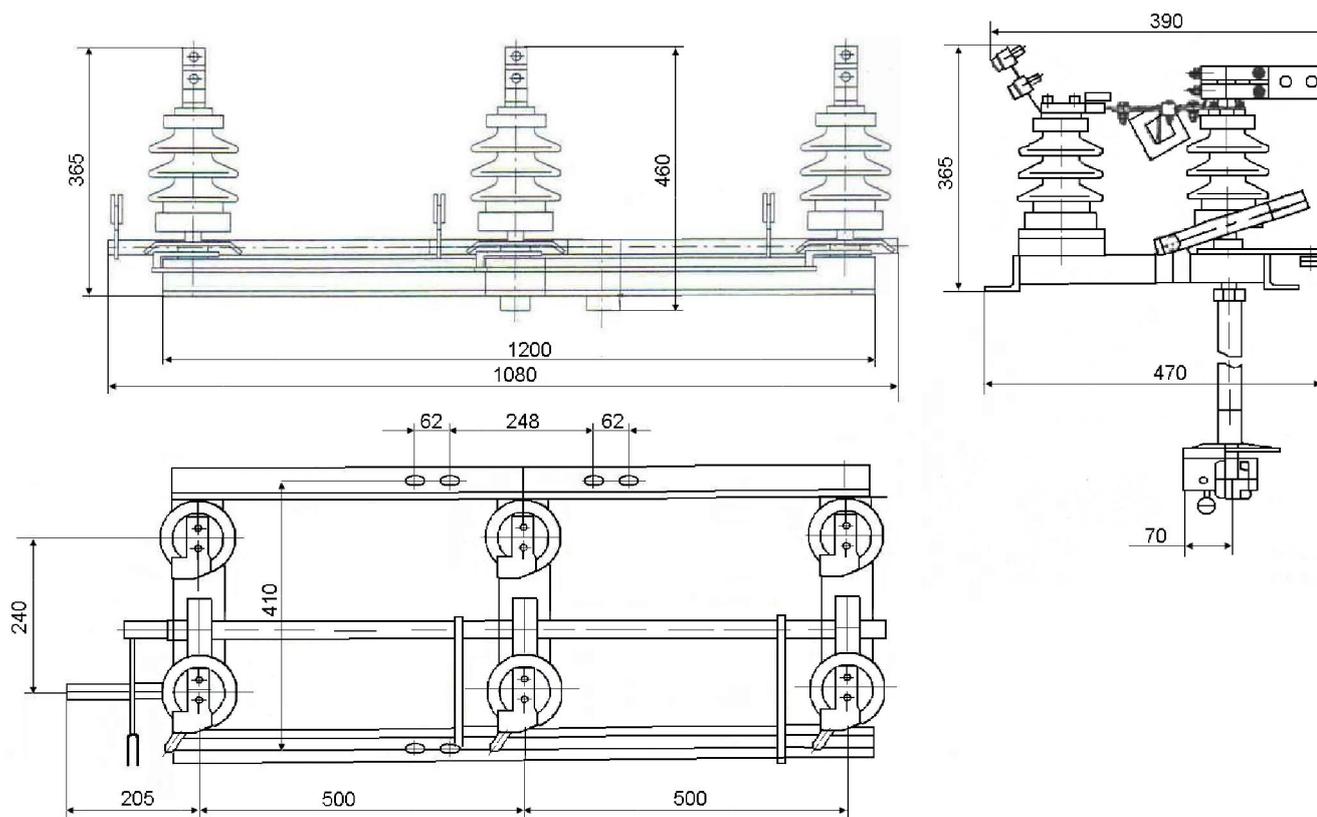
Габаритные размеры разъединителя РЛНД-1-10
